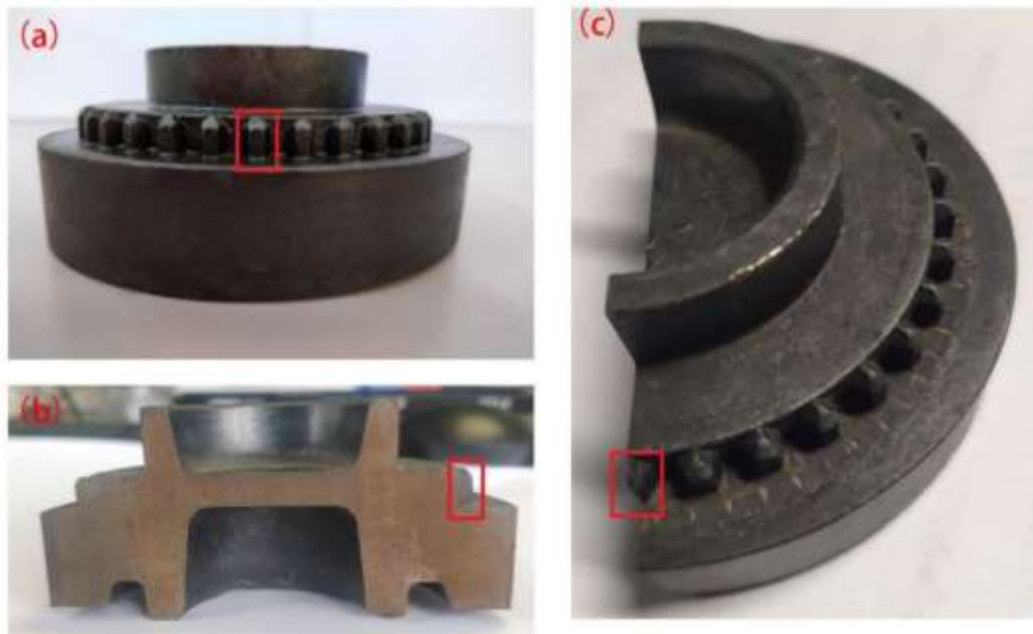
Соединительная шестерня после горячейковки: (а) соединительная шестерня; (б) поперечный разрез через зубья; (в) осевой вид. [5]
